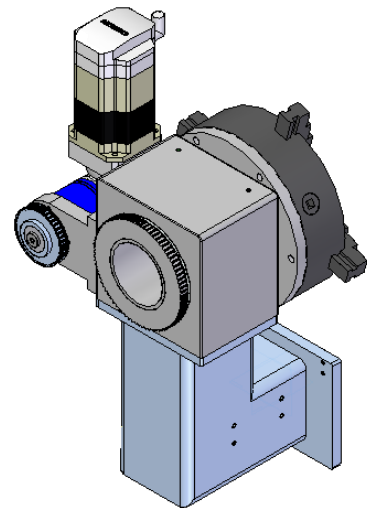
Estrutura de tubo de aço soldada para o suporte bucha.
